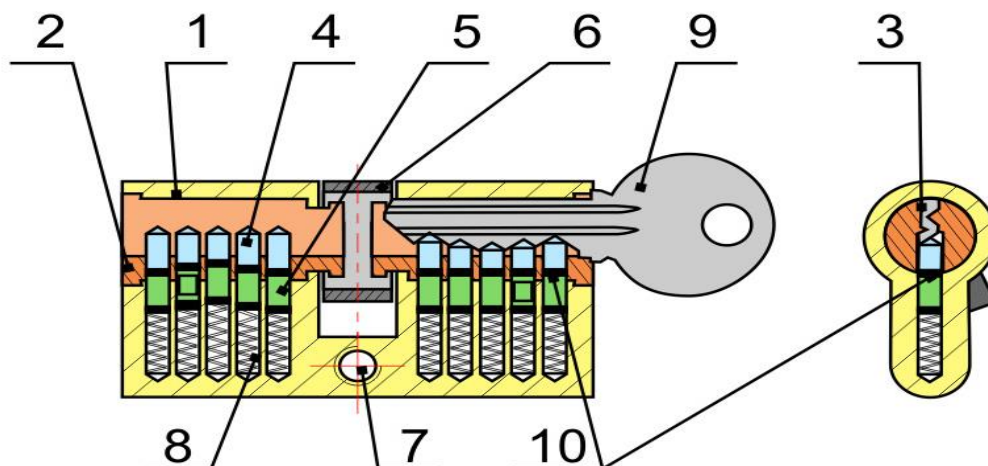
Схема штифтового блока секрета цилиндрического замка: 1 – корпус цилиндрического механизма, 2 – цилиндр (ротатор) с кодовым механизмом, 3 – скважина для ключа, 4 – кодовые штифты, 5 – запирающие штифты (плунжеры), 6 – поводок, 7 – крепёжное отверстие, 8 – пружина, 9 - ключ, 10 – линия разделения между корпусом и цилиндром (ротатором)
